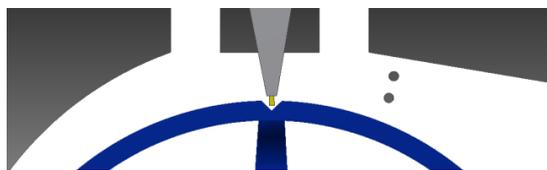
Detalhe da fresta do tambor e cerdas da roda de cola
